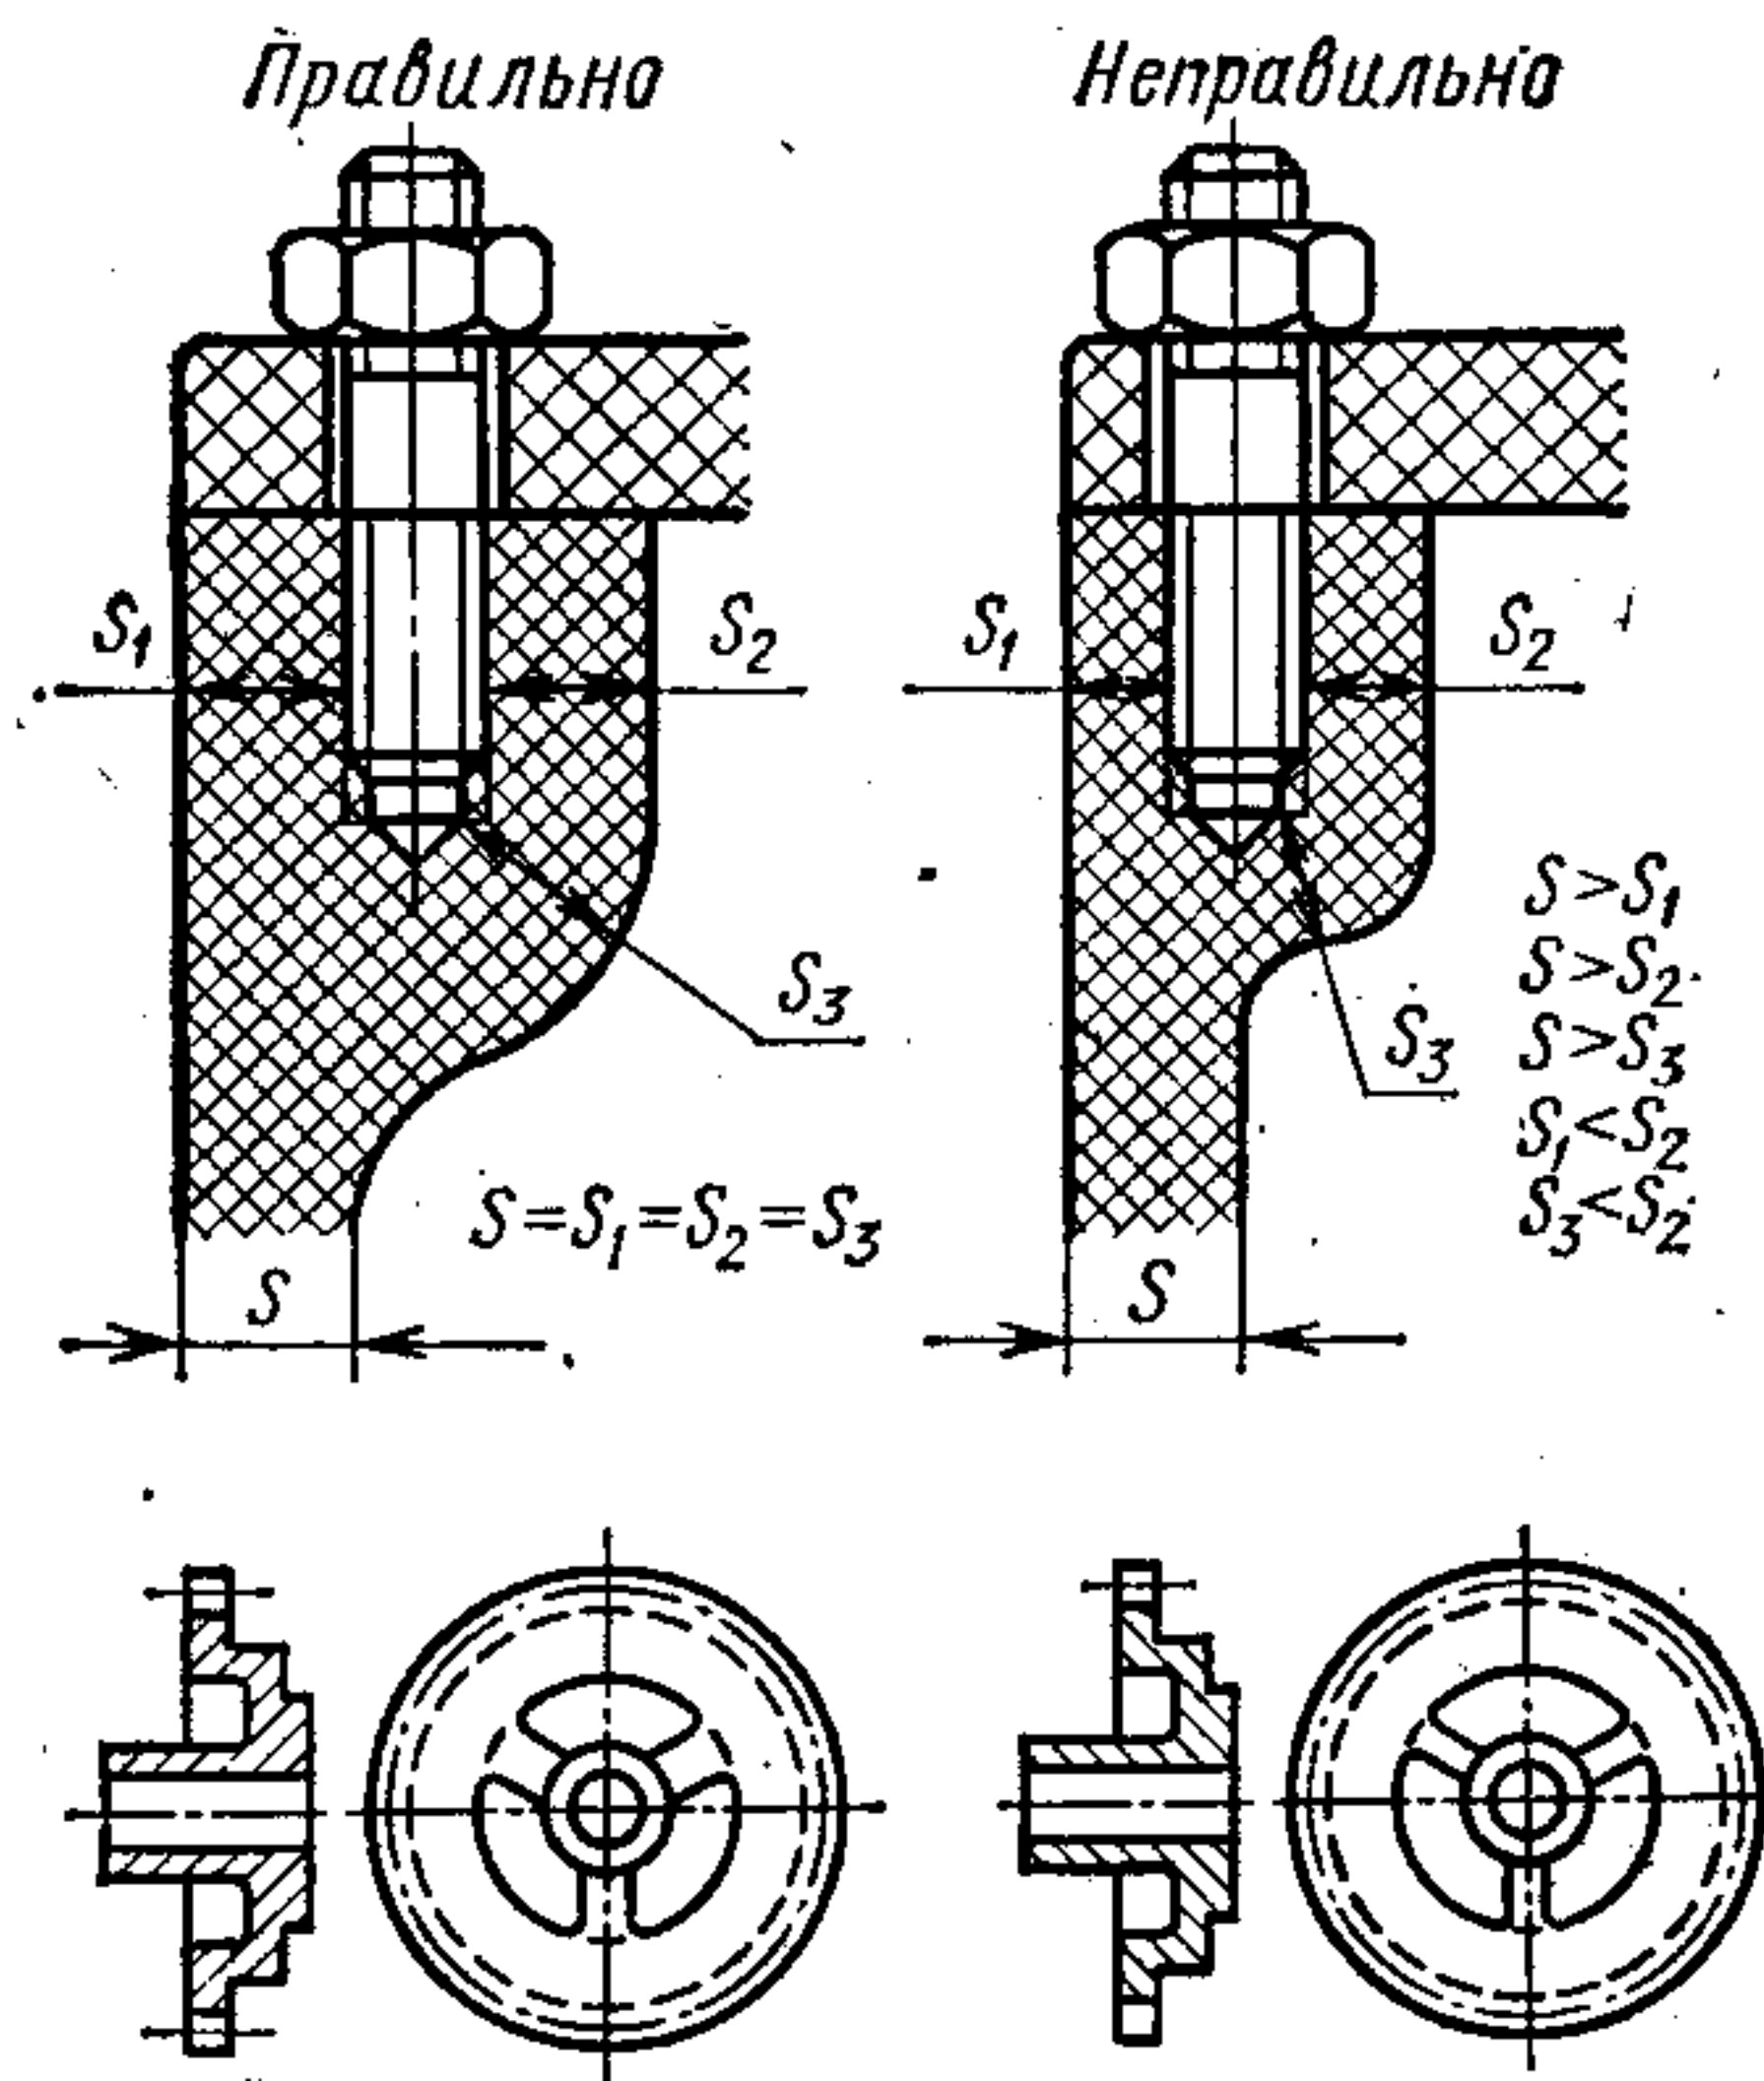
Примеры конструкций приливов под шпильку и зубчатых колес
